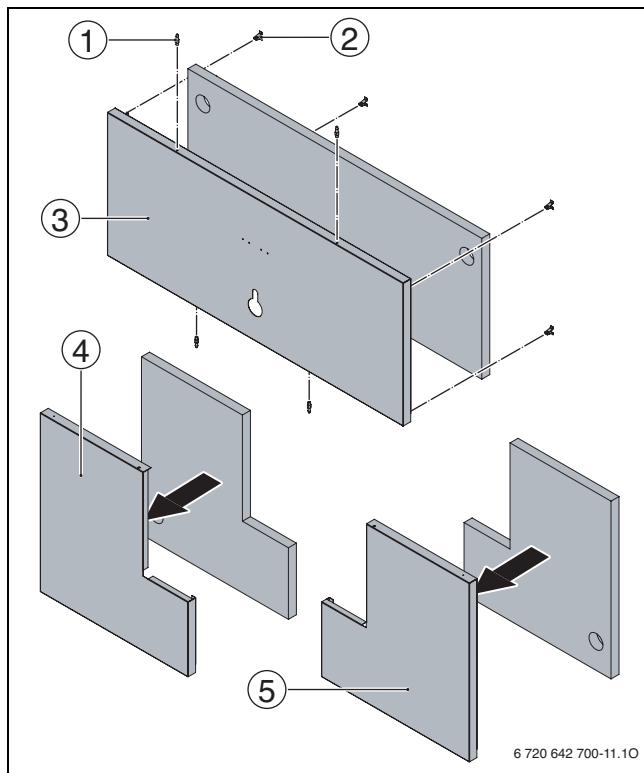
Установка обшивки двери у котлов 1400 - 1850 кВт, второй этап
